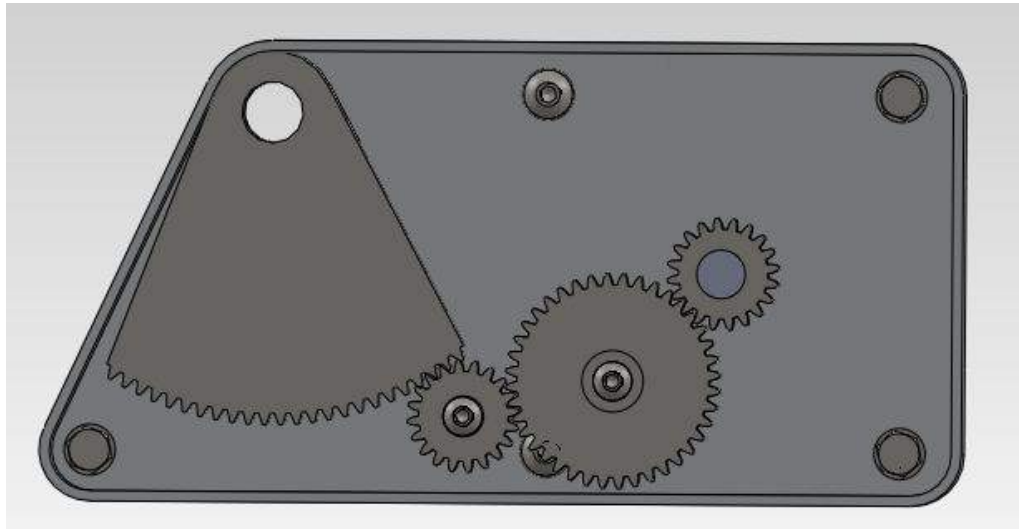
Disposición engranajes dentro de la reductora del eje horizontal.
